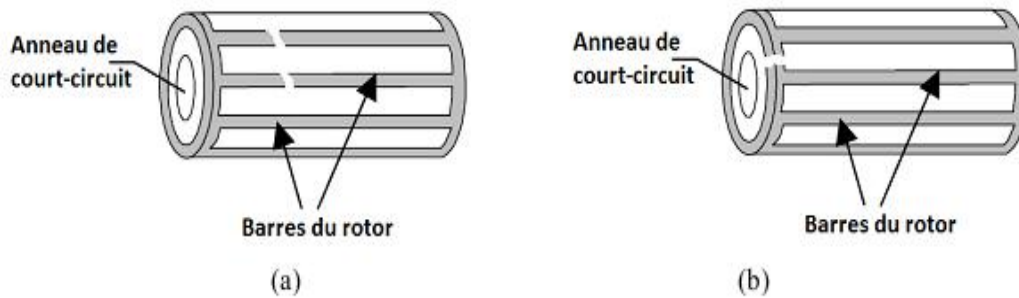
Défauts du rotor à cage : a) Rupture de barres ;
